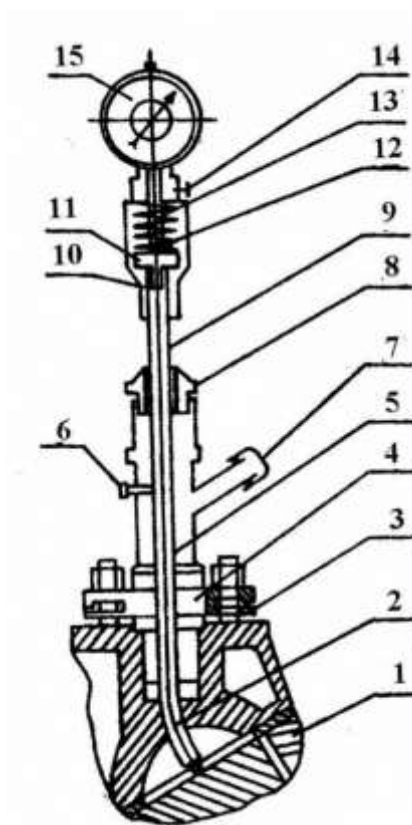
Индикатор перемещений поршня КИ-11140.
